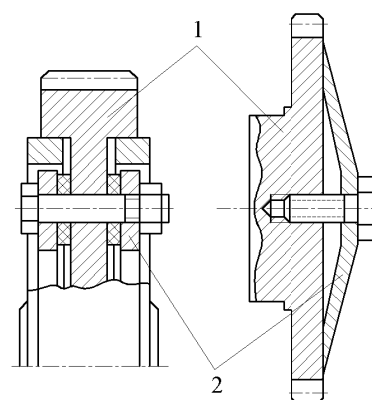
Зубчатые колеса с накладными и встроенными демпферами: 1 – зубчатые колеса; 2 – демпферы
